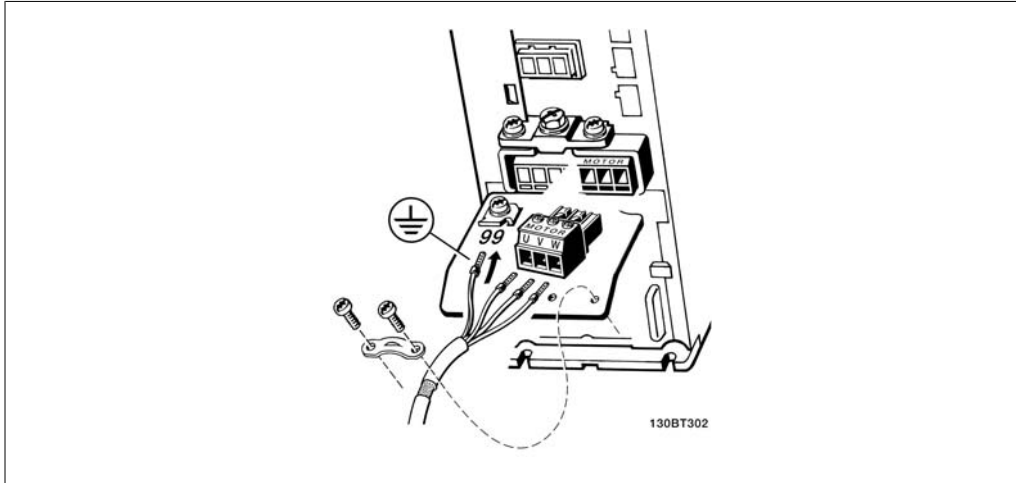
Подключение двигателей к преобразователям в корпусах A1, A2 и A3
